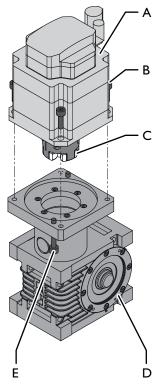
Motor entfernen: Getriebeeinheit Güdel
